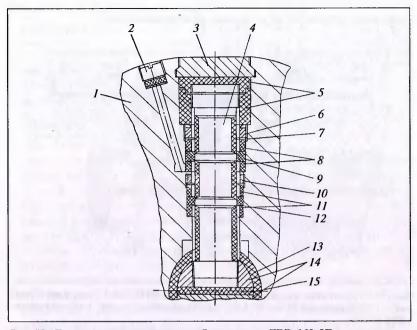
Болт токоподвода ротора турбогенератора ТВВ-160-2E: 1- вал ротора; 2- пробка; 3- клин; 4- токоведущий болт; 5- изоляционные прокладки; 6, 10- гайка; 7- шайба; 8, 11- уплотнительные шайбы; 9, 12- уплотнительные шайбы; 13- изоляционная втулка; 14- токоподвод ротора (две половины); 15- изоляционная прокладка
